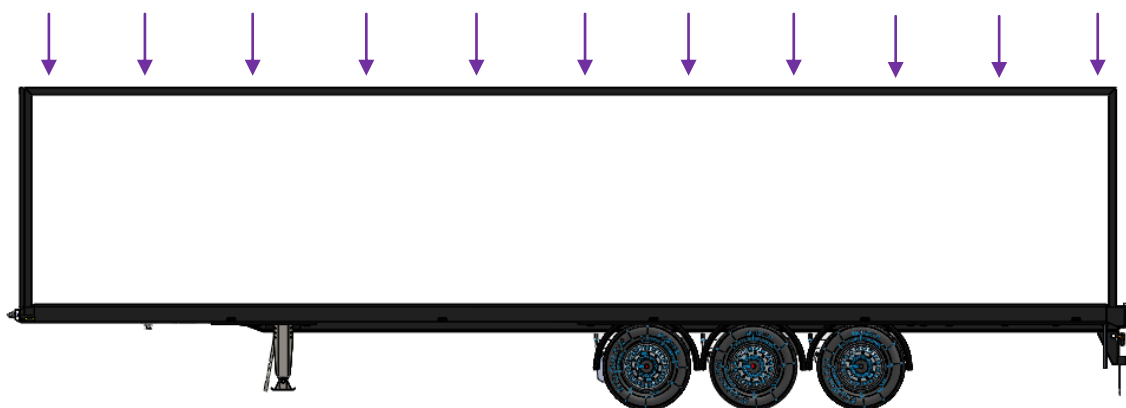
Cargas aplicadas sobre marco longitudinal.
